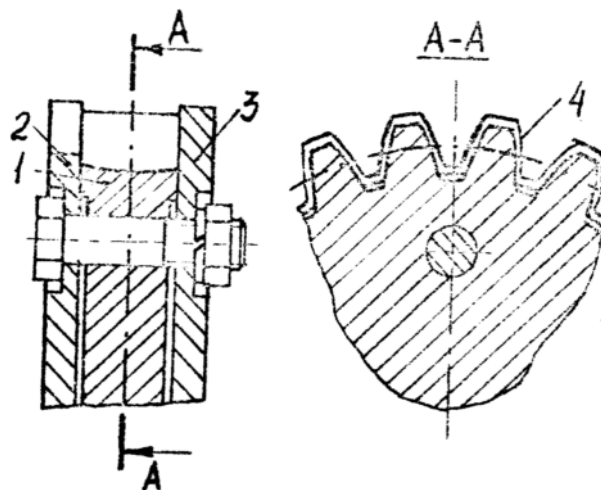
Инструмент для чистовой горячей накатки зубьев втулок.
